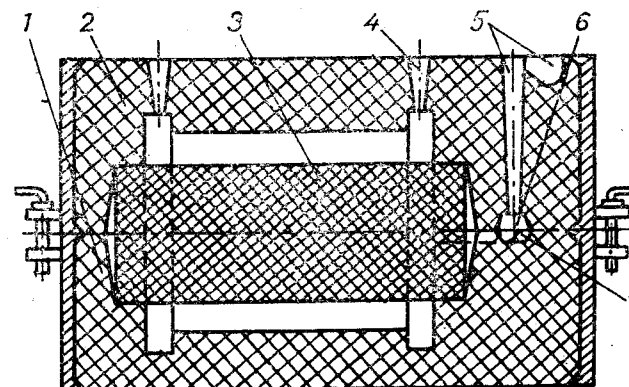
Піщано-глиняна форма для виготовлення вилівки втулки:
